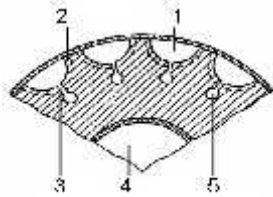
Схема сечения конденсатора с нарезками и капиллярными щелями
